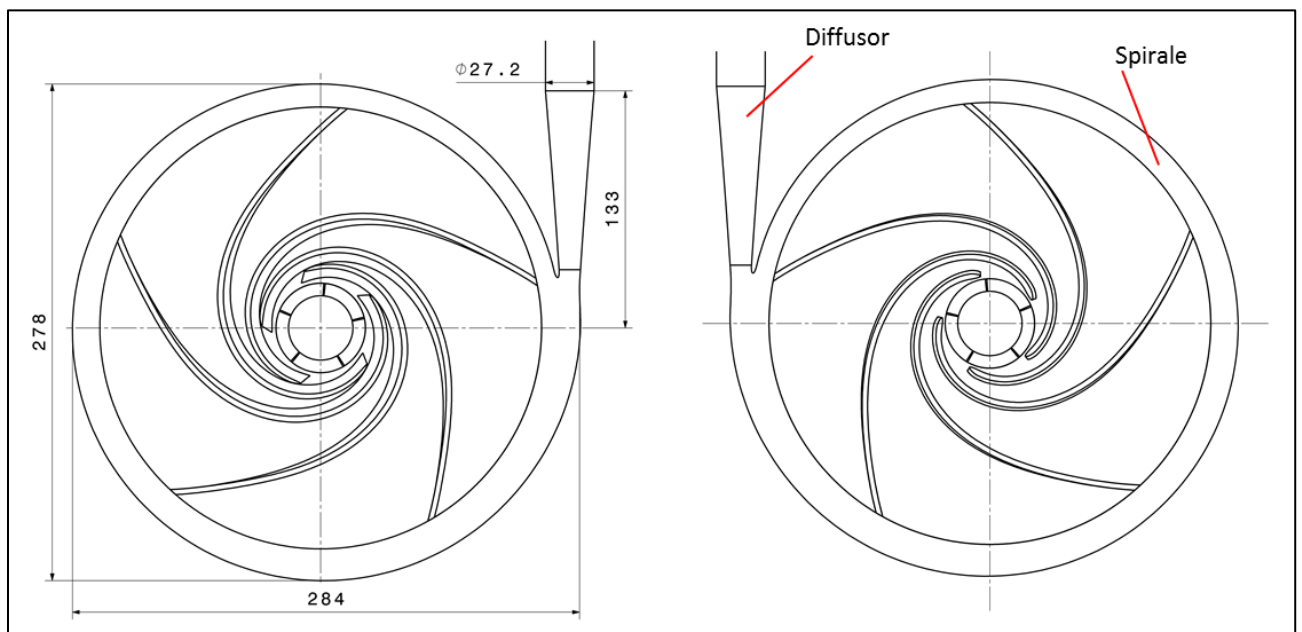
Draufsicht (links) und Rückansicht (rechts) der Pumpe für die mechanische Fertigung mit  $n_q = 6 \text{ min}^{-1}$
